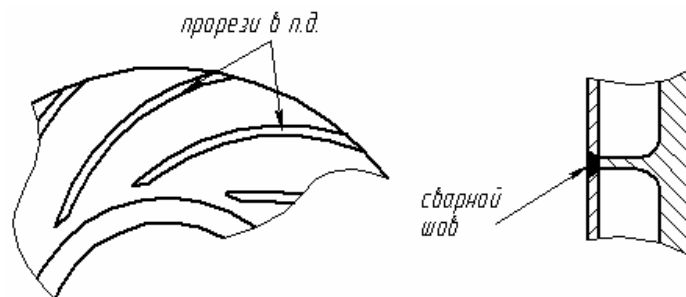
Схема сварки покрывающего диска и лопаток через прорези в покрывающем диске
